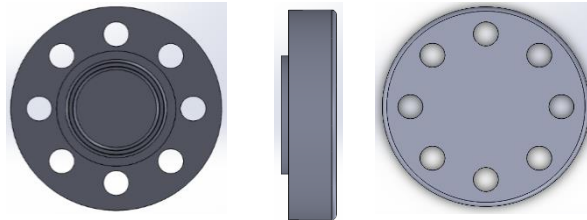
CAD de la Brida *Welding Neck* seleccionada.
